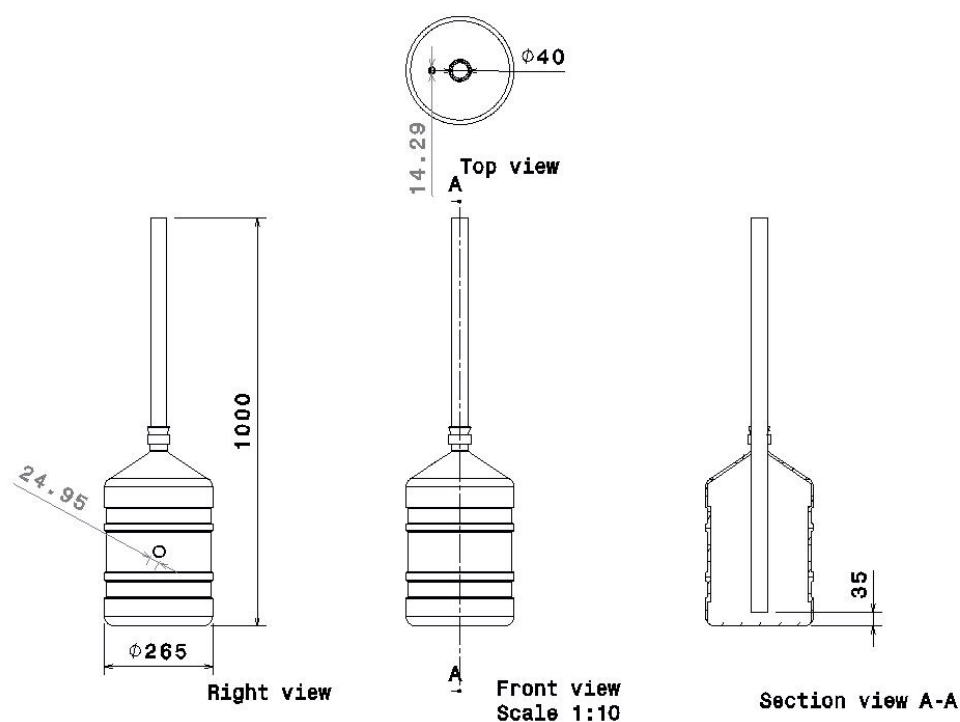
Vista frontal, superior, lateral e em Corte do biodigestor construído, dimensões em mm.
